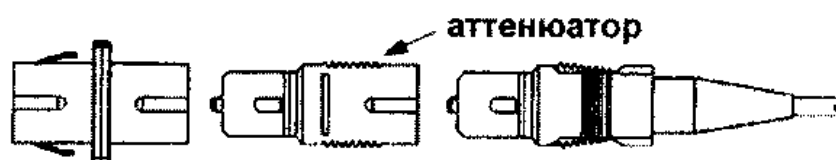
Внешний вид аттенюатора-FM розетки стандарта SC
